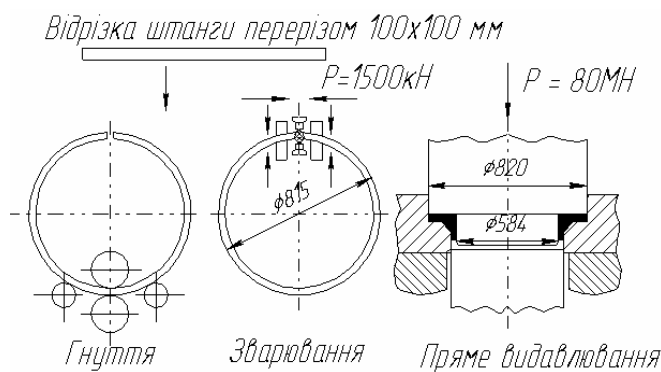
Операції виготовлення фланцевої деталі з гнутої зварної заготовки за [1]
